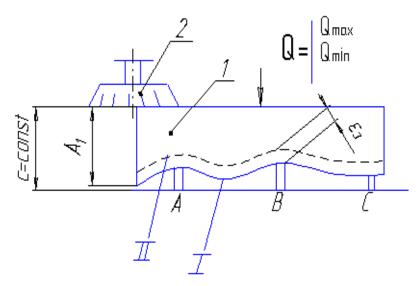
Схема, поясняющая непостоянство контактных деформаций заготовки и элементов приспособления
